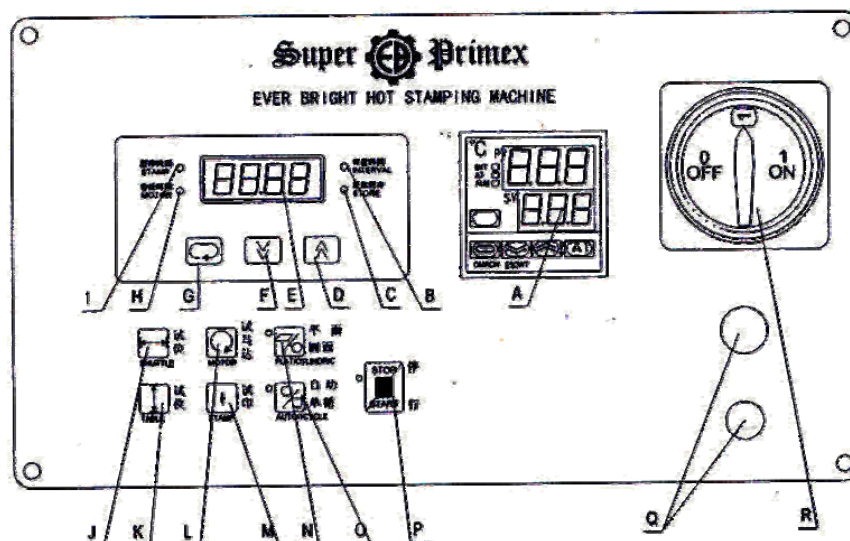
Робочий стіл для циліндричного штампування моделі H-200BS
